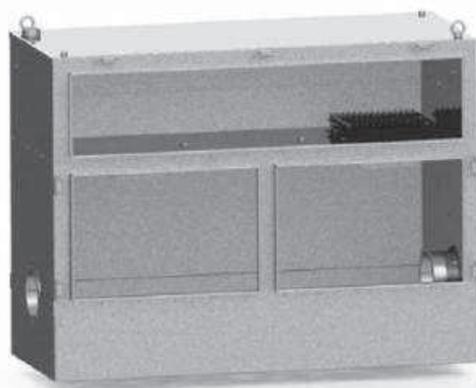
Шкаф трубный обогреваемый (ШТО)
